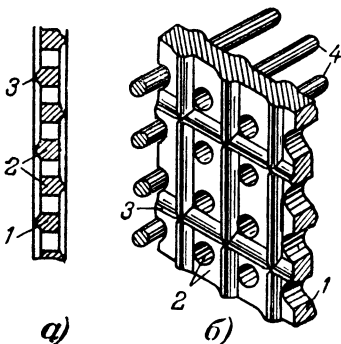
Часть ферритовой пластины с металлизацией и адресными шинами.
